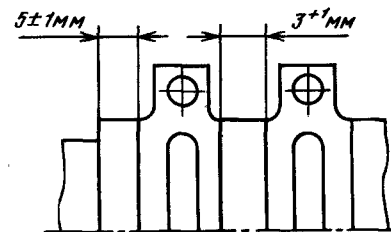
Схема крепления дюритовых и муфтовых соединений
